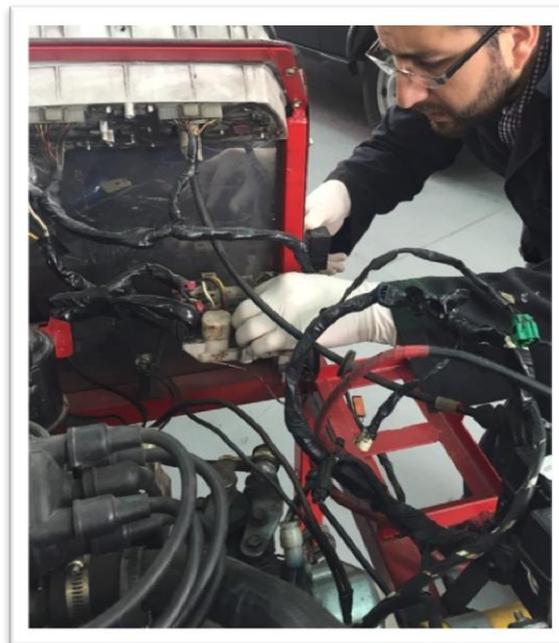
Instalación eléctrica tablero y caja de fusibles / Fuente: Propia del autor
